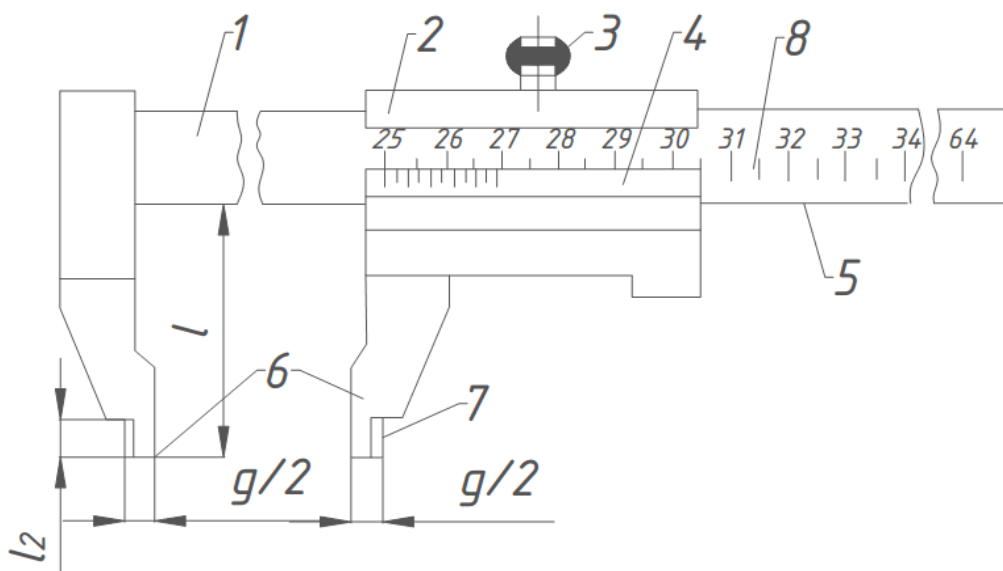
Штангенциркуль типа ШЦ–Ш:
